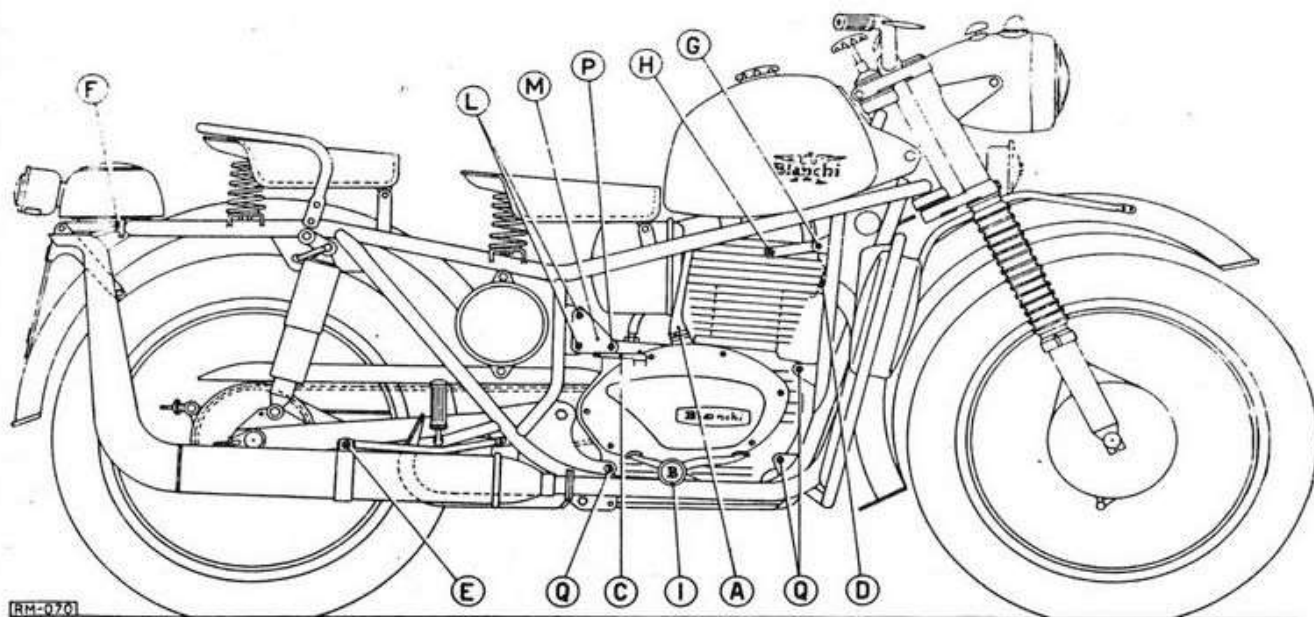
Rimozione del motore dal veicolo: parti da smontare sul lato destro
